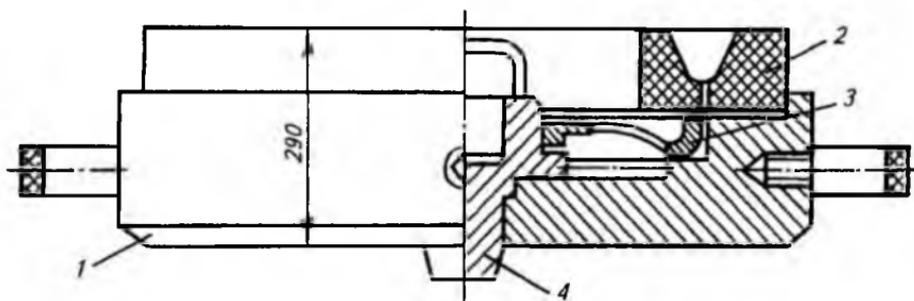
Схема кокиля для восстановления ведущего колеса заливкой жидким металлом:
